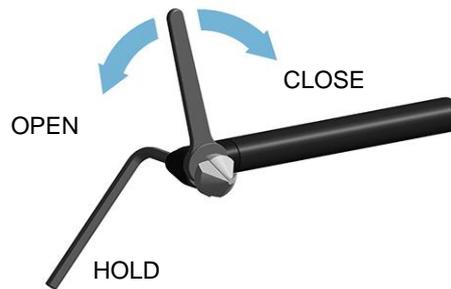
Tool change in model BEW 605 R, BEW 605 R SA
